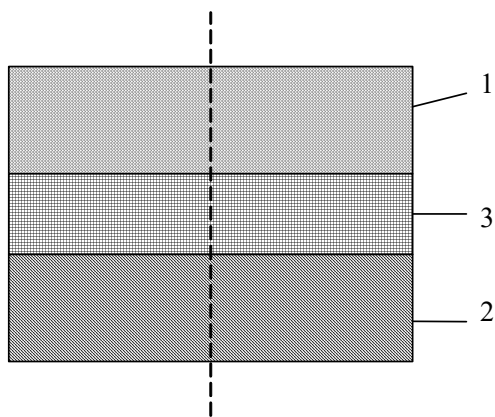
Схема паяного з'єднання: 1 – кераміка; 2 – метал;
